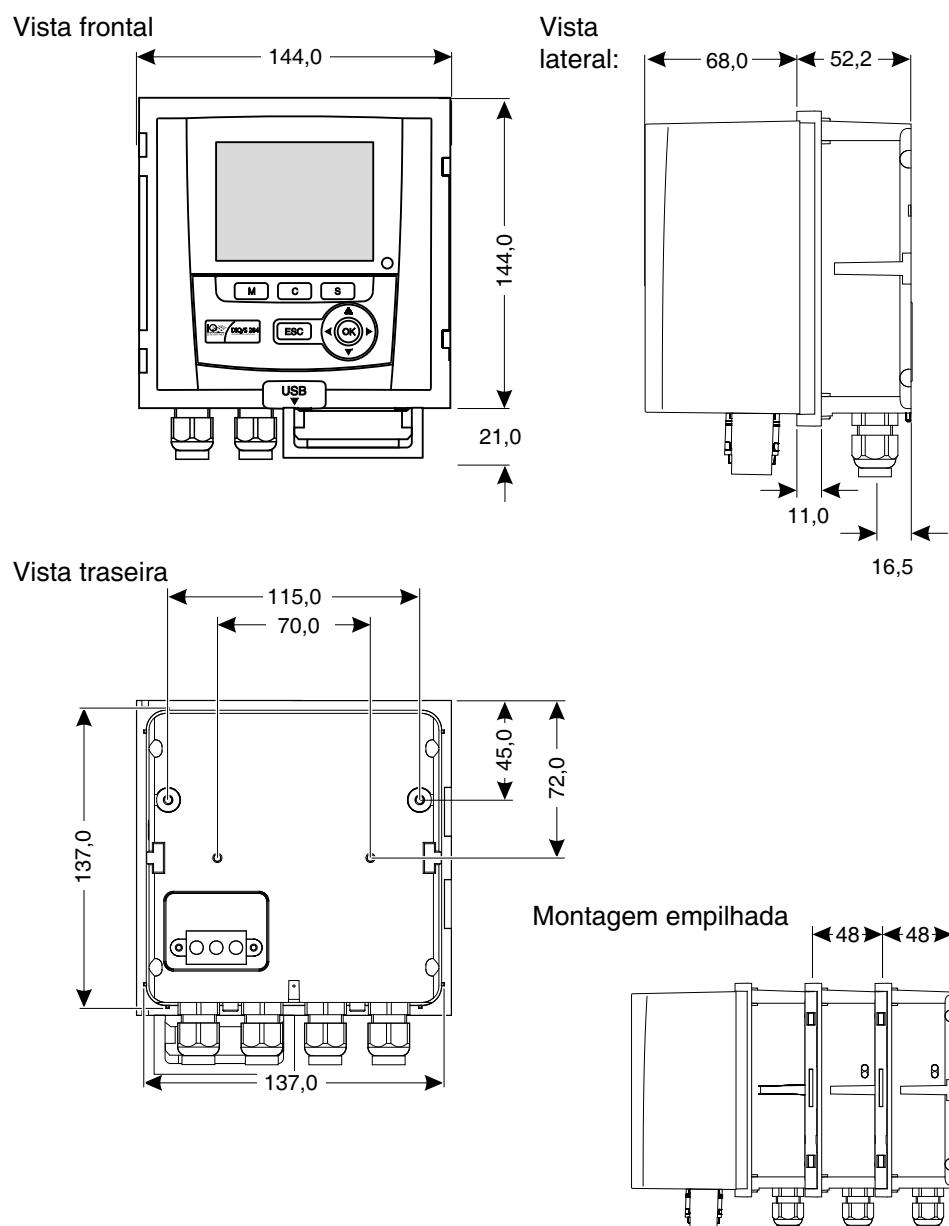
Desenho das dimensões DIQ/S 28X-MOD, DIQ/S 28X-PR (dimensões em mm)
